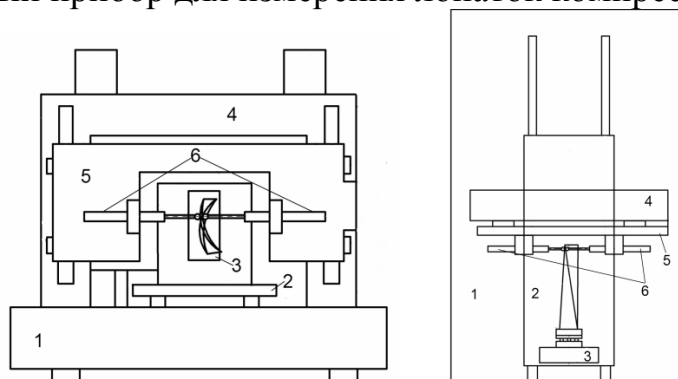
Схема прибора для измерения лопаток компрессора ГТД.
